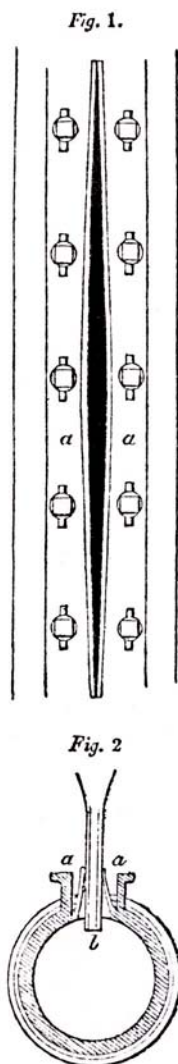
Válvula longitudinal propuesta por H. Pinkus (1834). Planta (fig. 1) y alzado (fig. 2). (Archivo RENFE).
